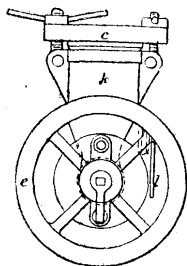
Vue de face du chargeur à échelle agrandie.
